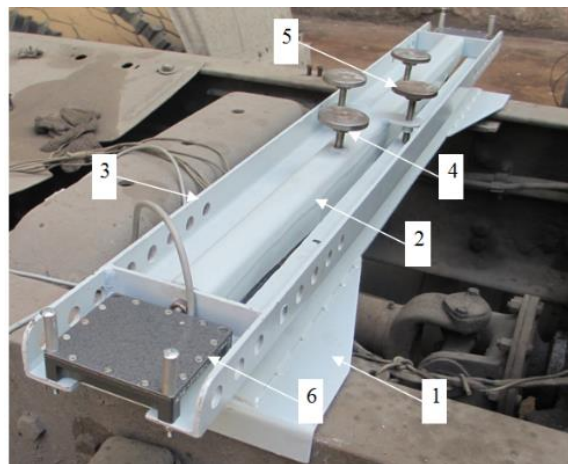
Приспособление для установки датчиков в нулевую отметку
